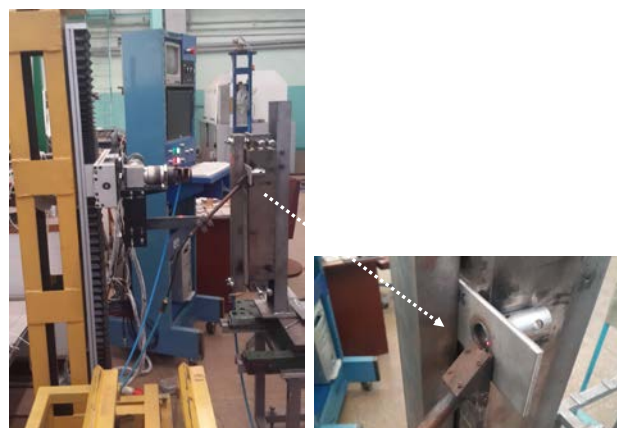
Лабораторний стенд (а) для експериментальних досліджень з лазерного зварювання кільцевих зварних з'єднань (б) з різномірних сталей у вертикальному просторовому положенні
